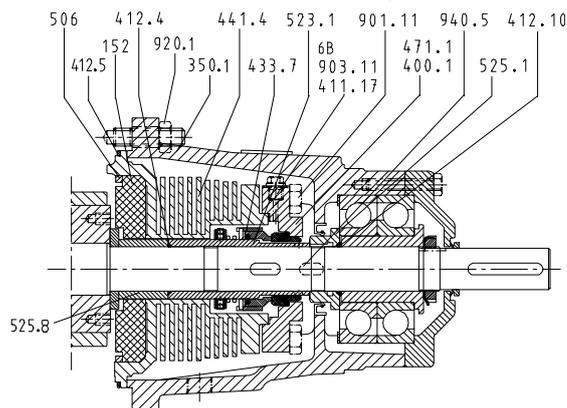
Desmontaje del cierre mecánico enfriado por aire
